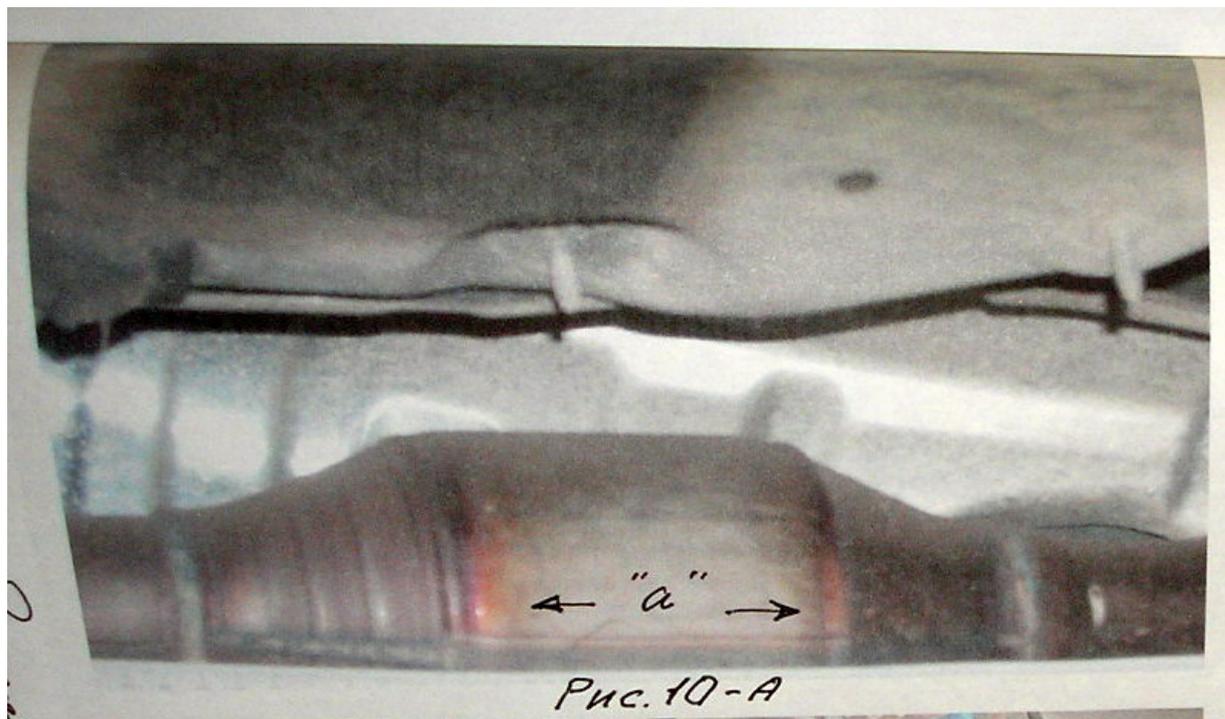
Фото корпуса нейтрализатора из заключения эксперта Ш-ва А.А. с ошибочным указанием на цвета побежалости в зоне сварных швов от сварки при производстве, как на признаки перегрева катализатора. На самом деле перегрева нет.
